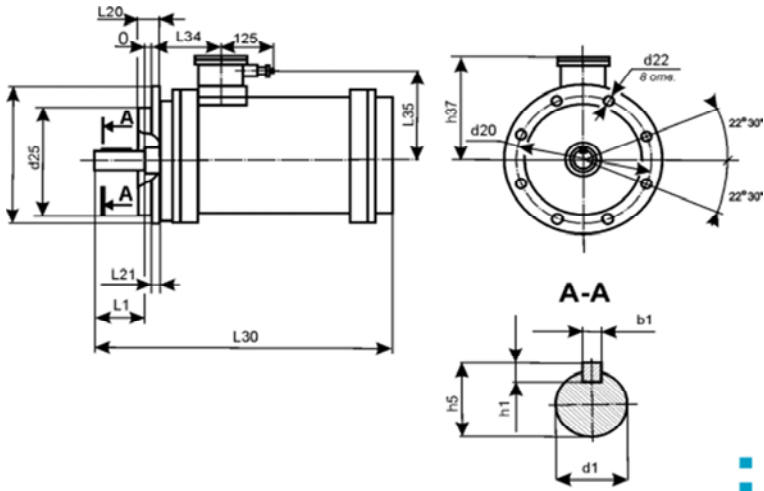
Габаритные размеры двигателей для приводов на АЭС
